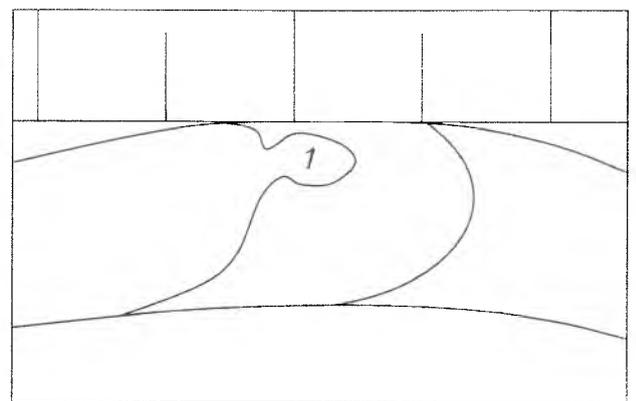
Подрезы (подрезы зоны сплавления) в стыковом сварном соединении трубопровода:
